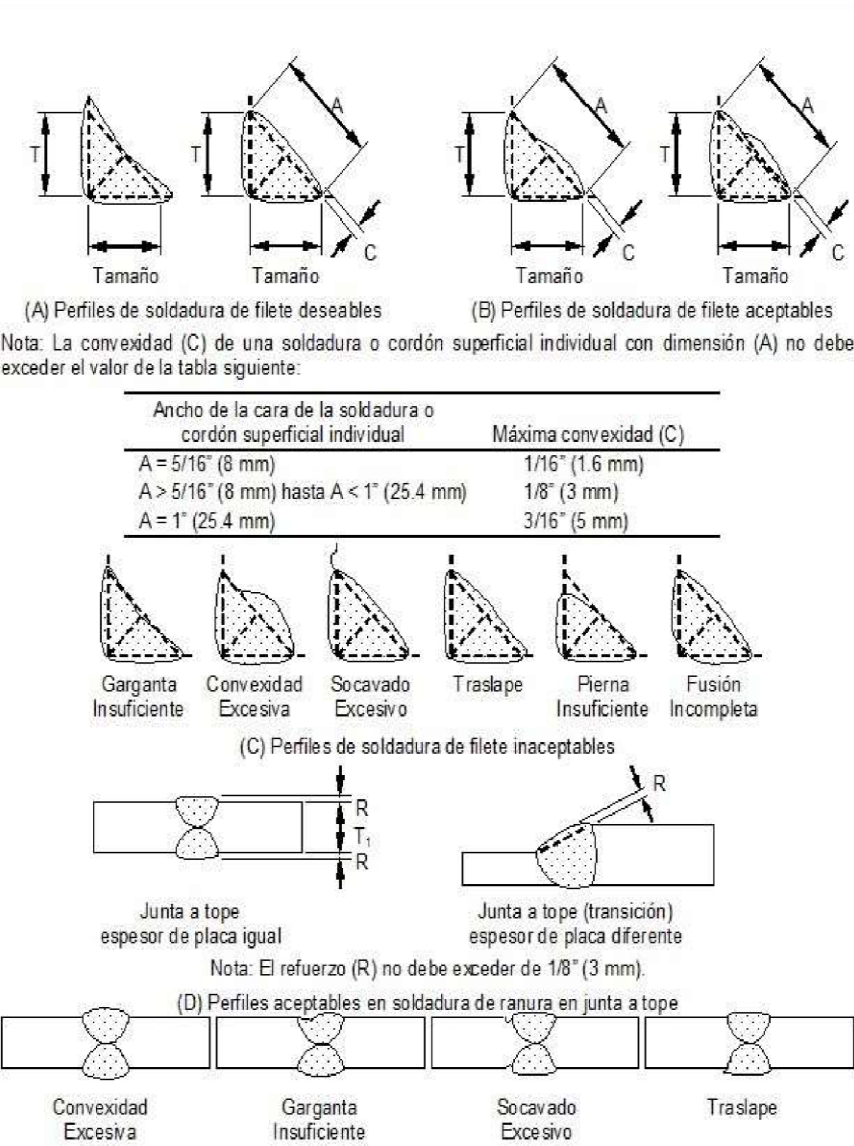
Perfiles inaceptables en soldadura de ranura en junta a tope.
